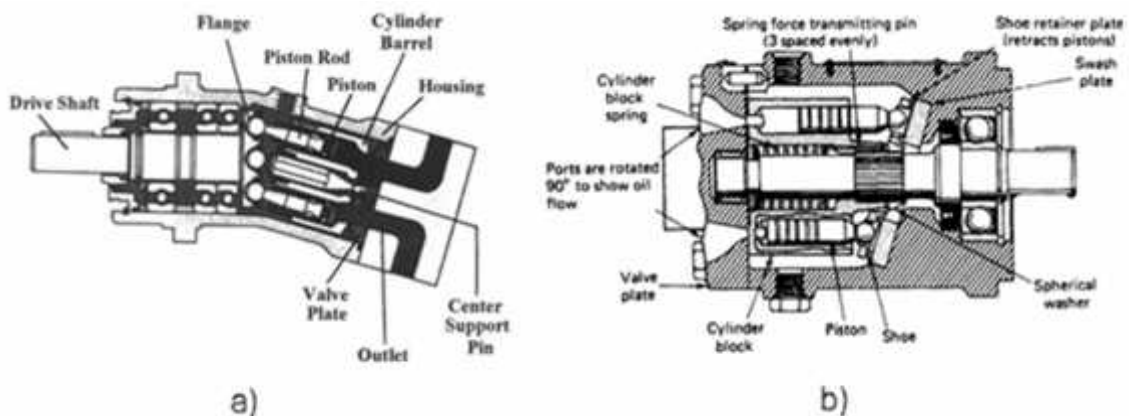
Bomba de pistones axiales (a) eje inclinado (b) plato basculante.
